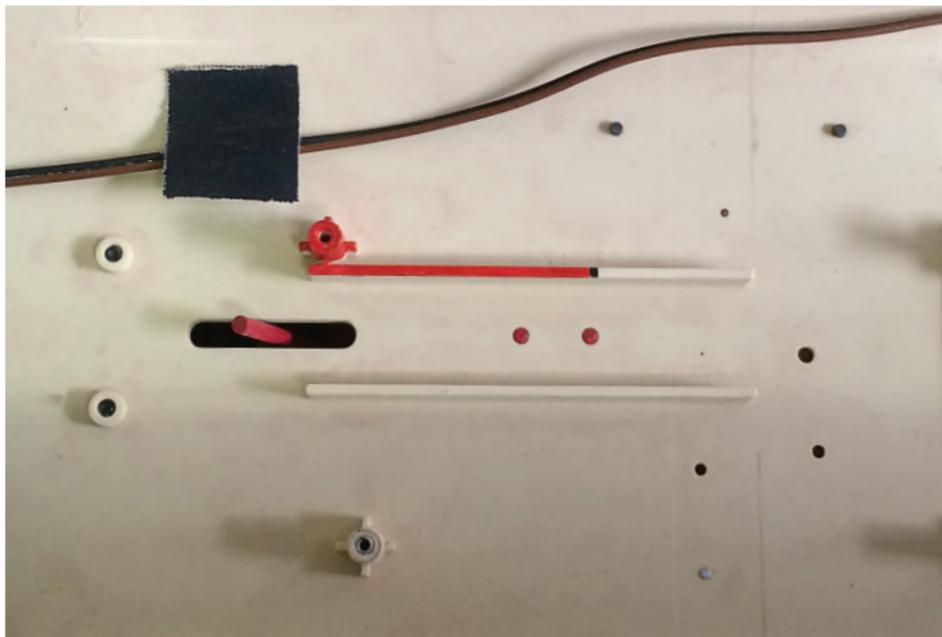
Stegbereich und Schraubenaufnahme (rot markiert) sind zu entfernen.
